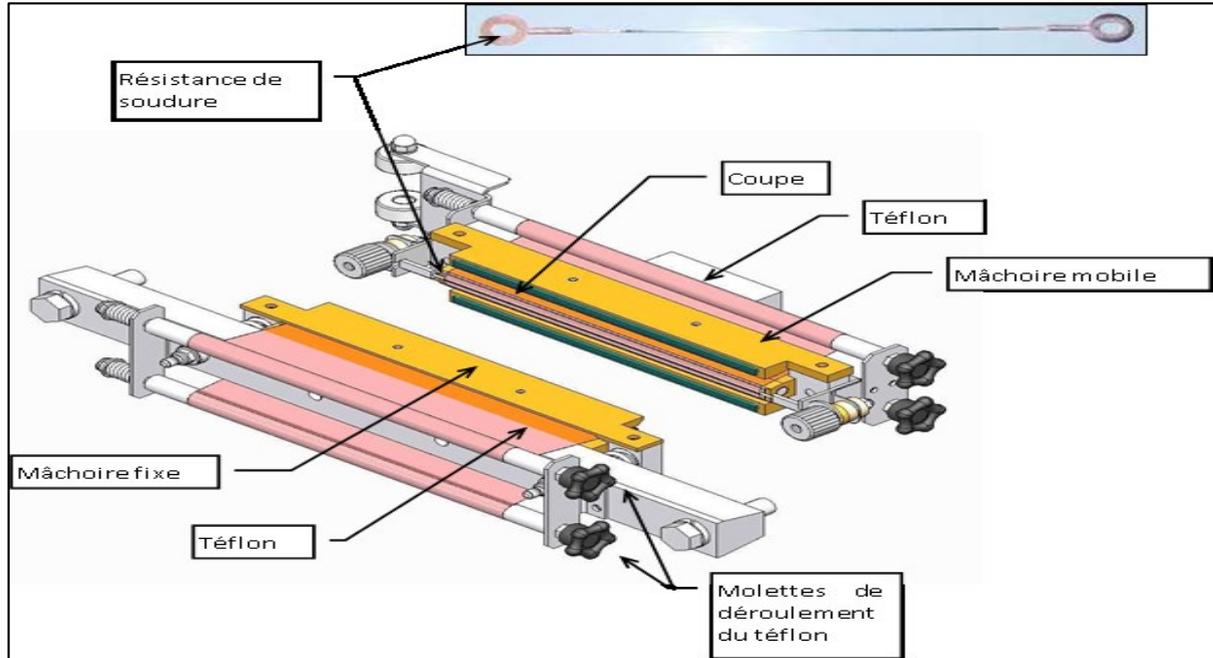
Système de Coupe-Soudure horizontale.[16]
